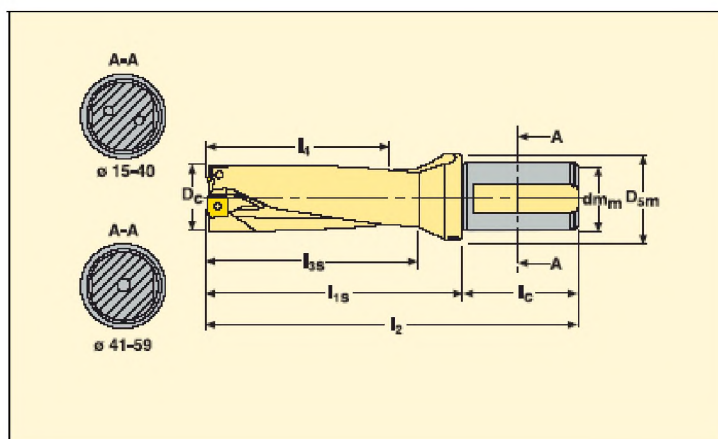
Свердло зі змінними твердосплавними пластинами
